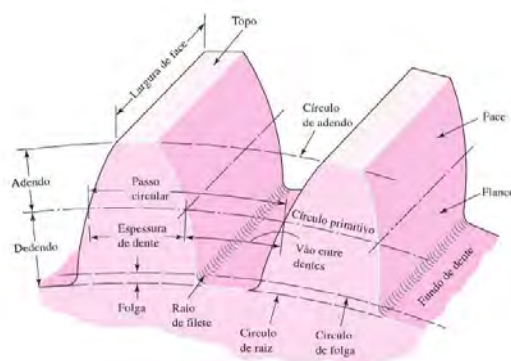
Nomenclatura para engrenagens cilíndricas de dentes retos [52]
